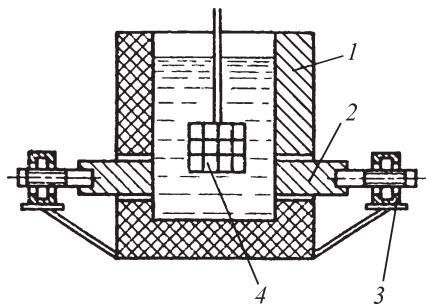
Однофазная печь-ванна для нагрева заготовок в соляном растворе
